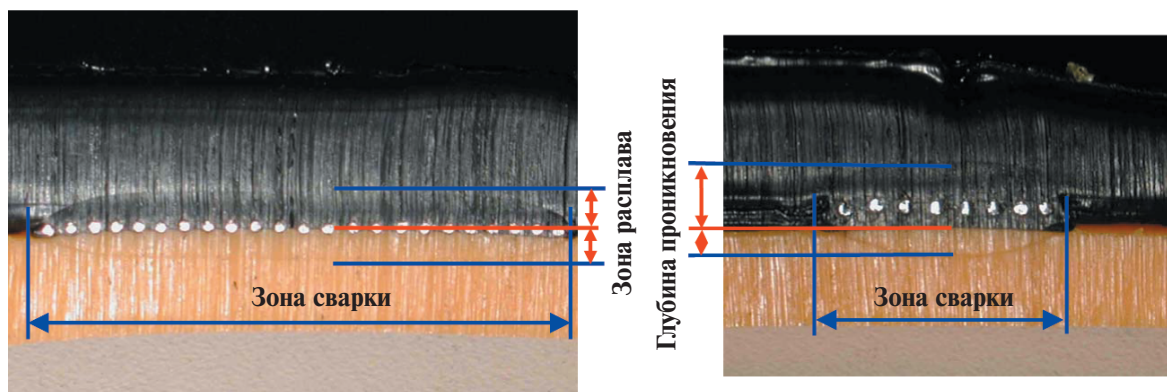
Приблизненно симметричный сварной эллипс для фитингов с открытой нагревательной спиралью и асимметричный — для фитингов с закрытой спиралью.
